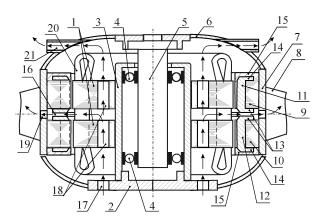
Конструкция двухпакетного AMB с экранированными короткозамыкающими кольцами ротора
